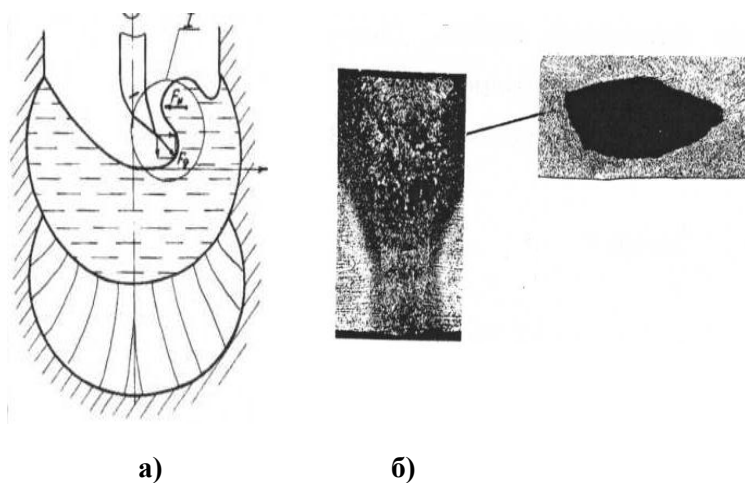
Перемещение гребня вытесненного металла сварочной ванны при колебаниях дуги (а) и макрошлиф сварного шва с дефектом несплавления (б)
